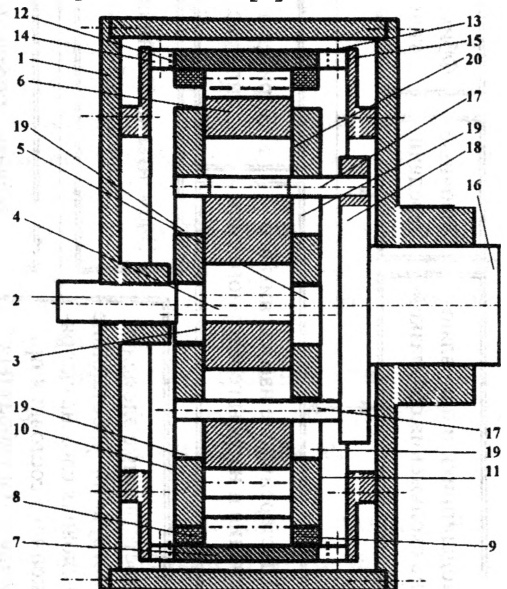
Комбинированная планетарная передача: 1 – корпус; 2 – входной вал; 3, 4, 5 – эксцентрики; 6 – сателлит; 7 - гибкий деформируемый обод с внутренними зубьями; 8, 9 - кольцевые канавки; 10, 11 - нажимные ролики; 12, 13 - торцевые зубчатые полумуфты на гибком ободе; 14, 15 - торцевые зубчатые полумуфты на боковых крышках корпуса; 16 - выходной вал; 17 - пальцы; 18 - фланец выходного вала; 19 - овальные сквозные отверстия; 20 - цилиндрические сквозные отверстия
